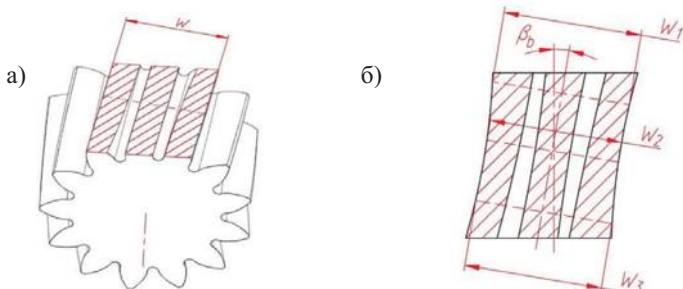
Формирование погрешности измерений длины общей нормали при измерении универсальным инструментом а) 3D модель зубчатого цилиндрического зубчатого колеса, б) сечение плоскостью, касательной к основному цилиндру, где W_2 – искомый минимальный размер длины общей нормали, W_1 и W_3 – показатели длины общей нормали в крайних сечениях.
